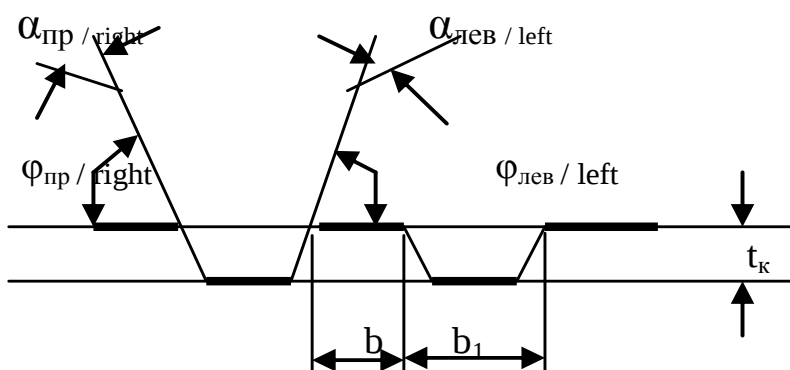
Профиль режущих кромок, образованный пересечением основной режущей кромки вспомогательными винтовыми поверхностями
